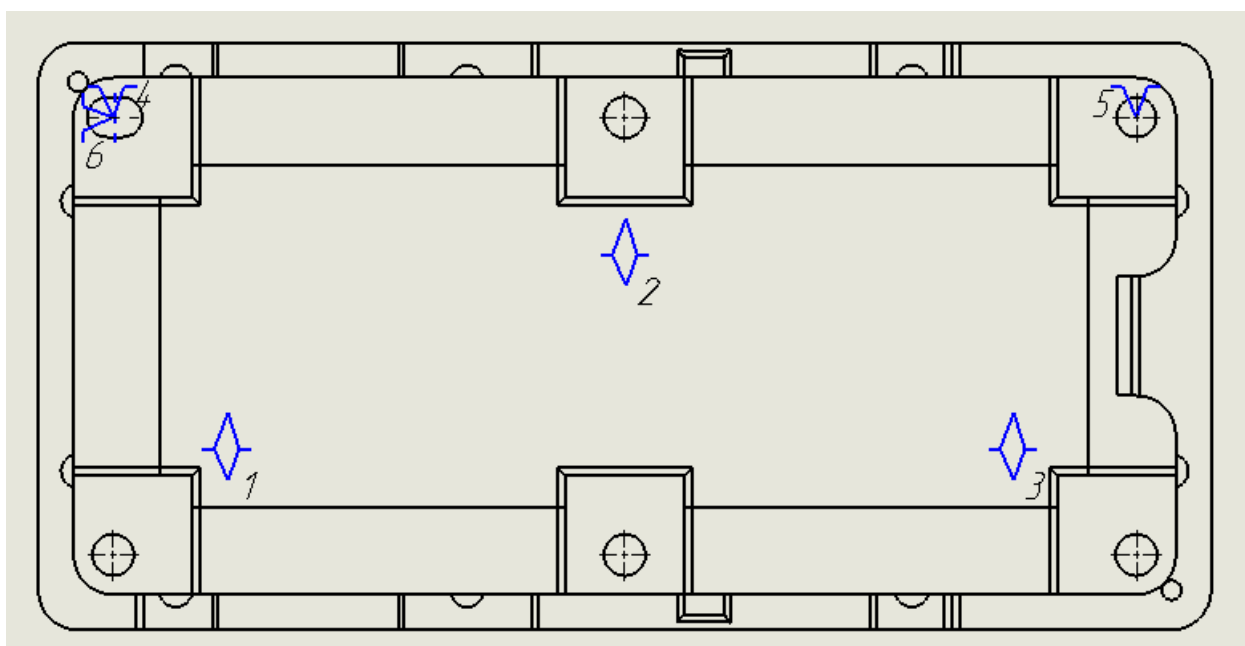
Схема установки корпуса редуктора для обработки отверстий под подшипники для валов  $\varnothing 80H7(+0,025)$  мм и  $\varnothing 52H7(+0,025)$  мм
